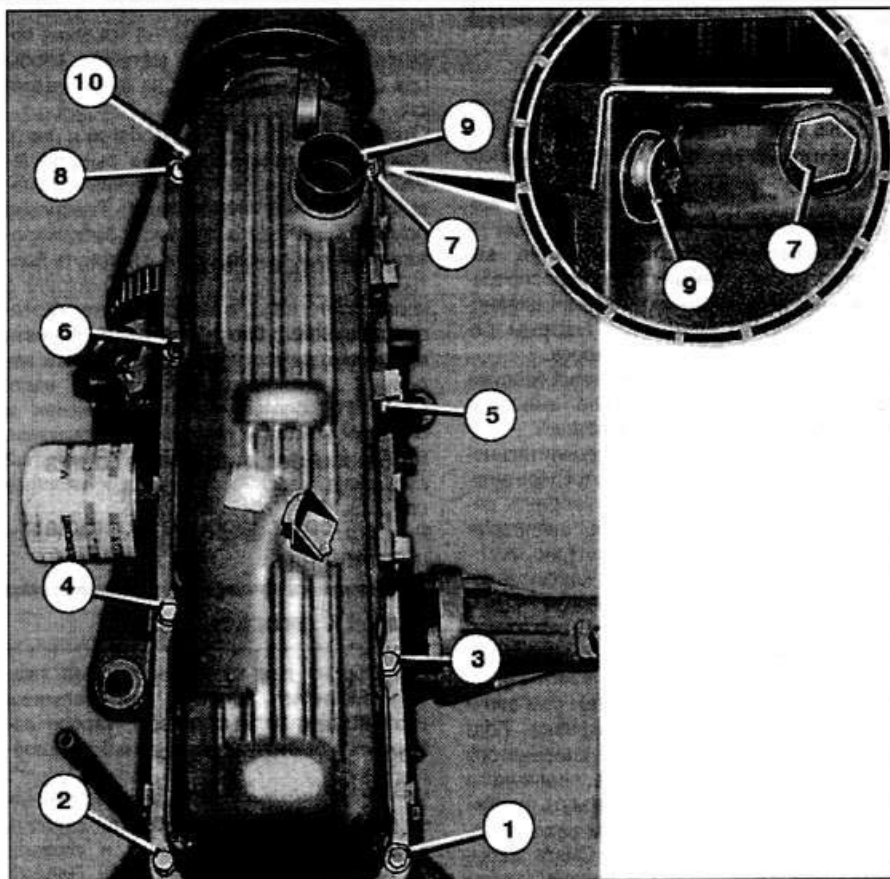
Порядок затяжки болтов крышки головки цилиндров
